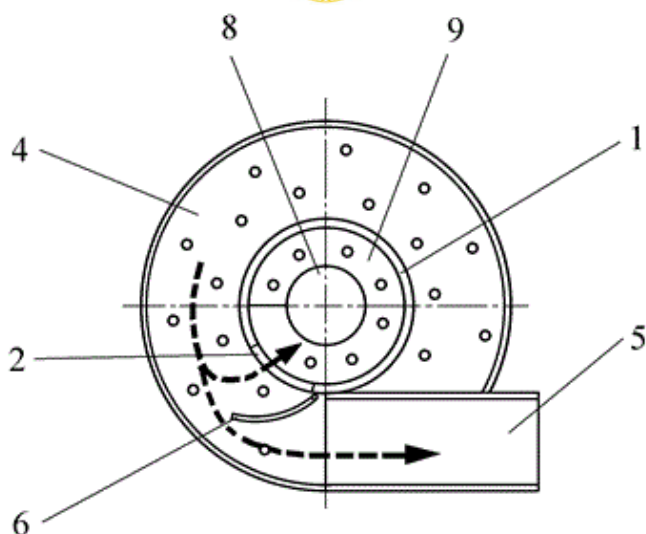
Смеситель № 2. Вид сверху: 1 — бункер; 2 — отверстие; 4 — желоб; 5 — выгрузочный патрубок; 6 — подвижная заслонка; 8 — цилиндрическая вставка; 9 — лопасть
